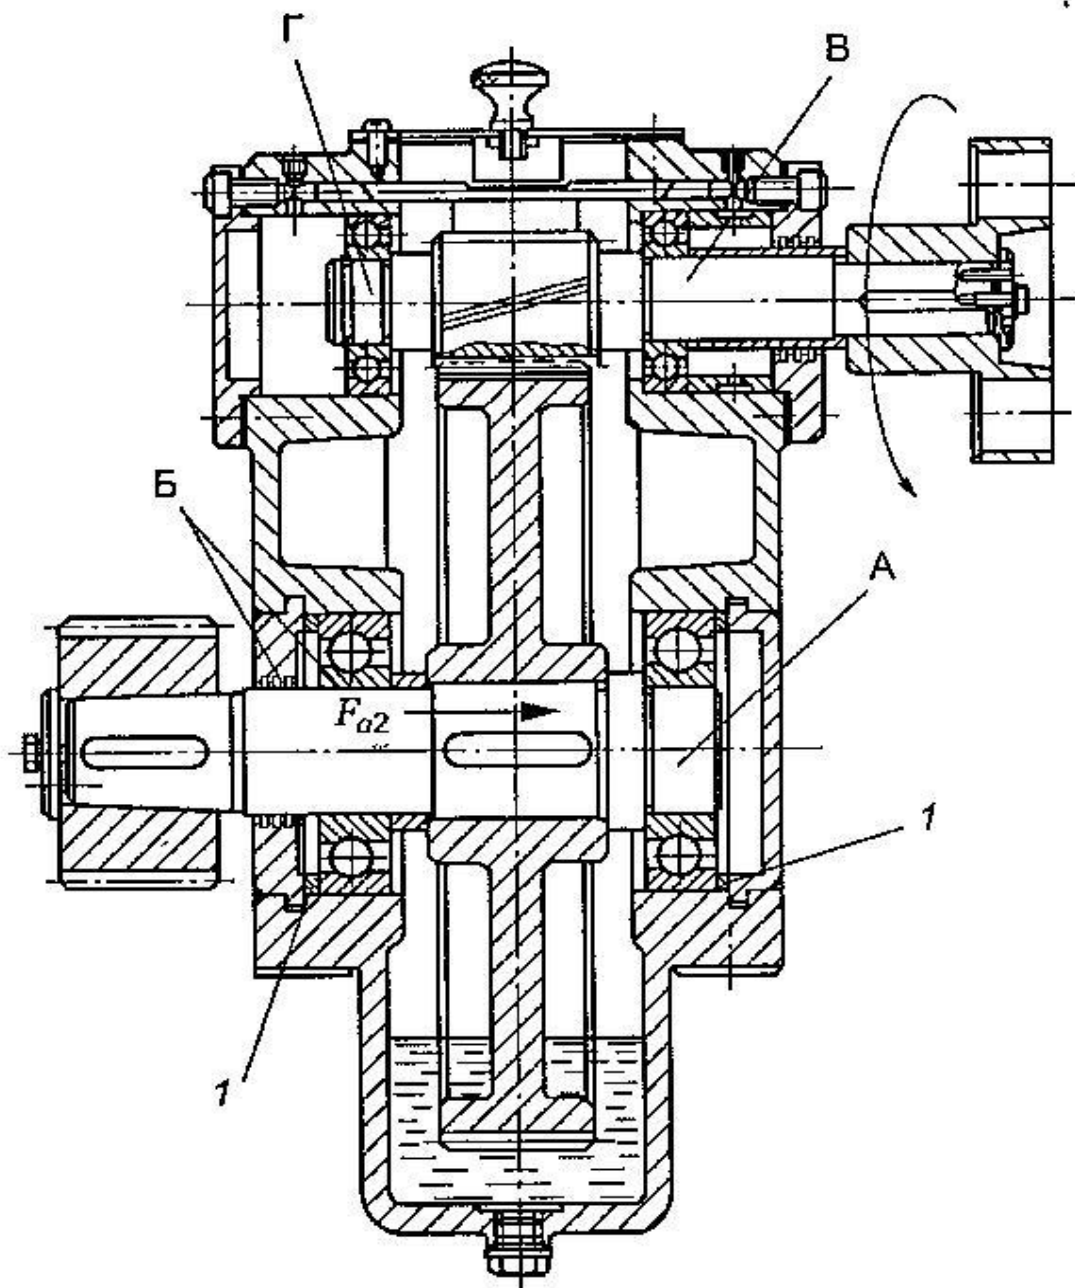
Цилиндрический одноступенчатый редуктор, вертикальное исполнение!5
